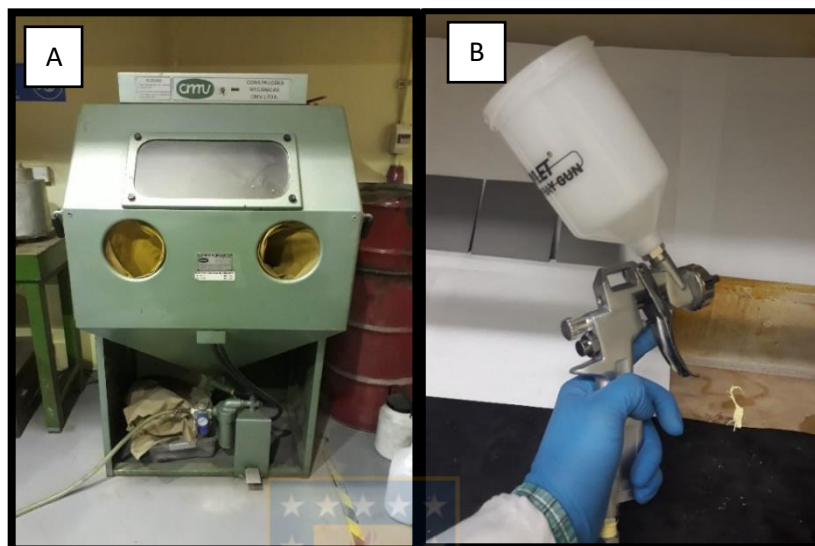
[A] Máquina de arenado, [B] pistola a presión S-990G. Fuente propia
